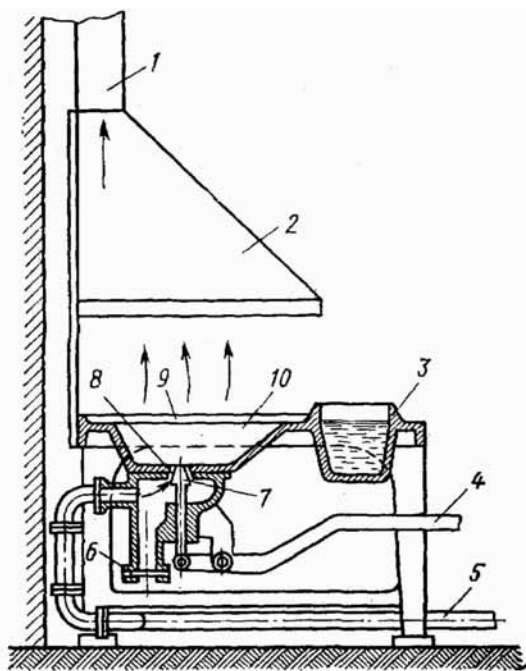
Стационарный одноочаговый кузнечный горн открытого типа: 1 – вытяжная труба; 2 – зонт; 3 – бачок с водой для закалки инструмента; 4 – рычаг для регулирования подачи воздуха; 5 – воздухопровод; 6 – заслонка; 7 – конический накопчик; 8 – фурма; 9 – стол; 10 – очаг
